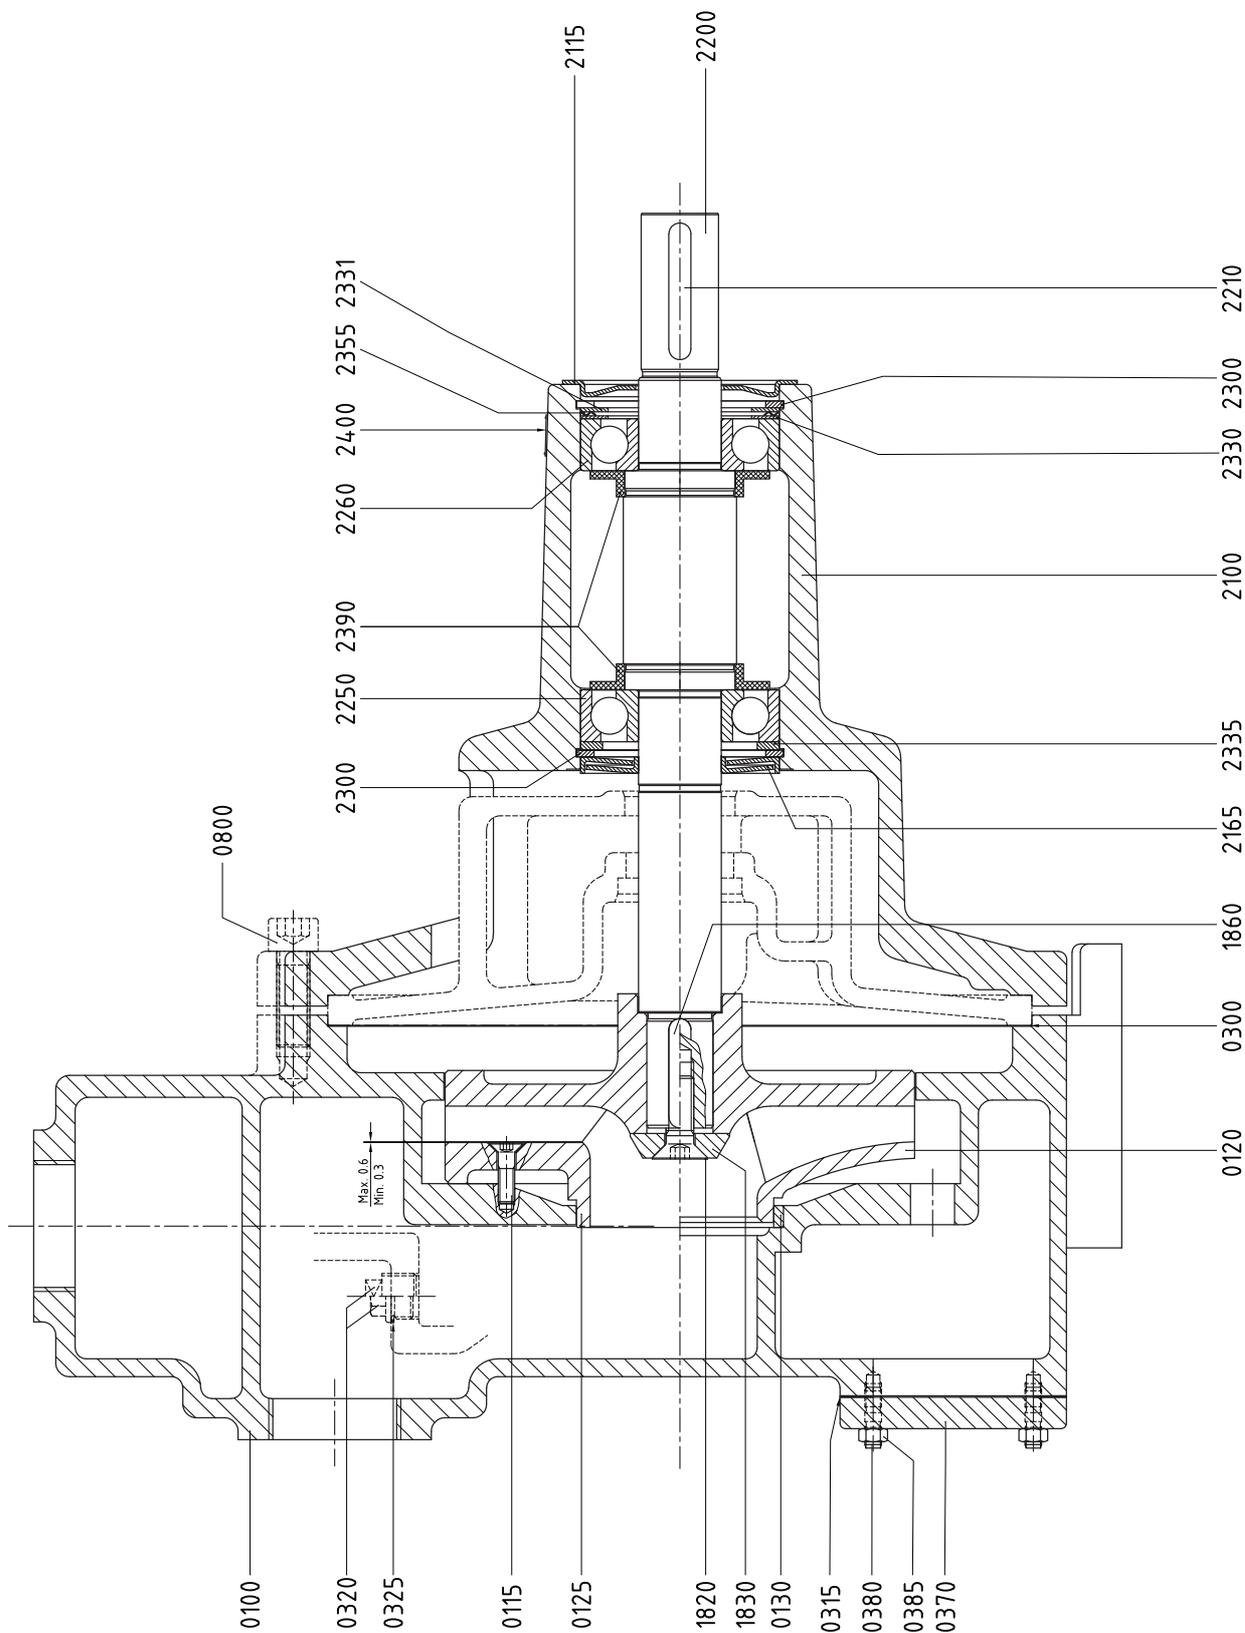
Plano seccional FRE - soporte del cojinete 3.
